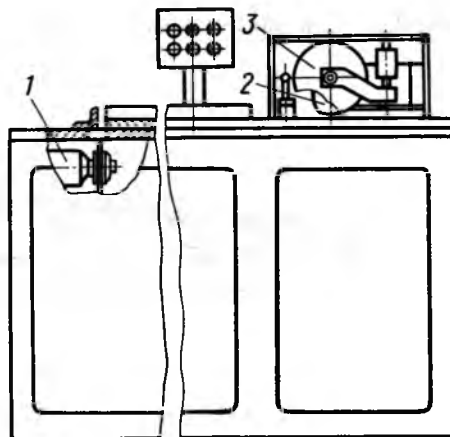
Станок для снятия свесов облицовочного материала щитов небольших размеров:
